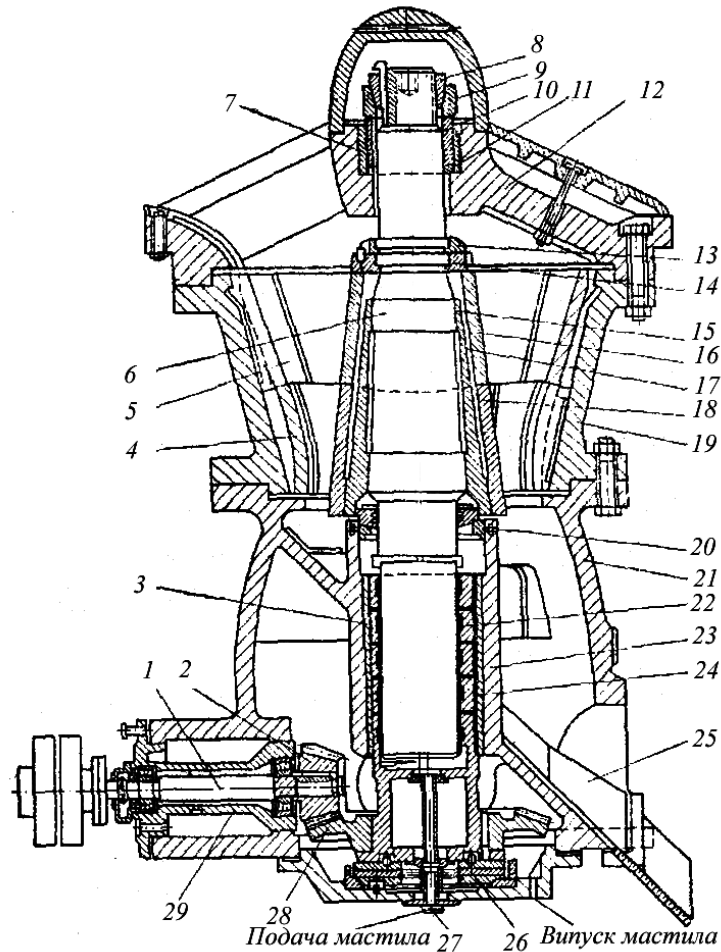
Конусна дробарка для грубого дроблення:
